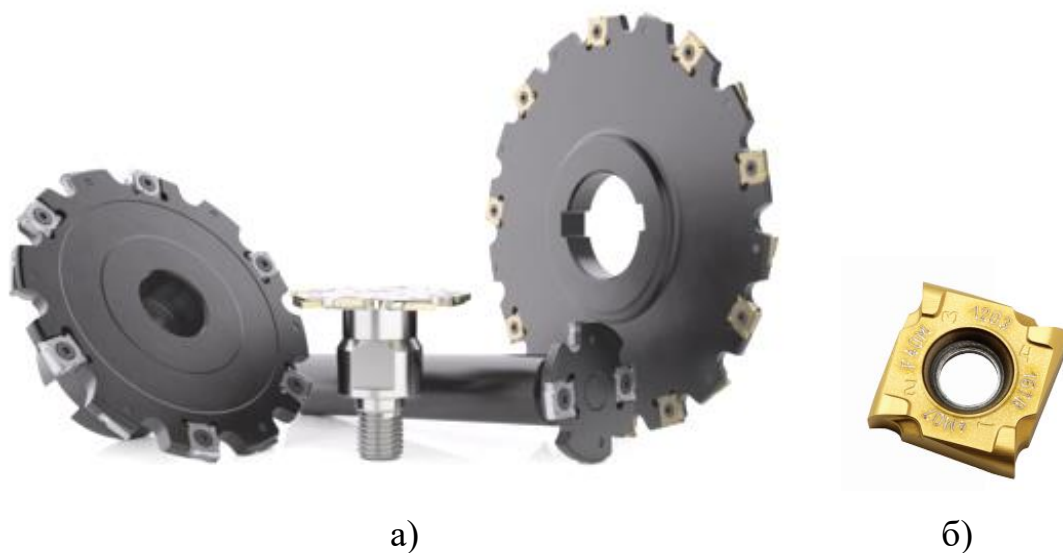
Відрізни дискові фрези а) та ріжуча пластина б) компанії Seco [15]
